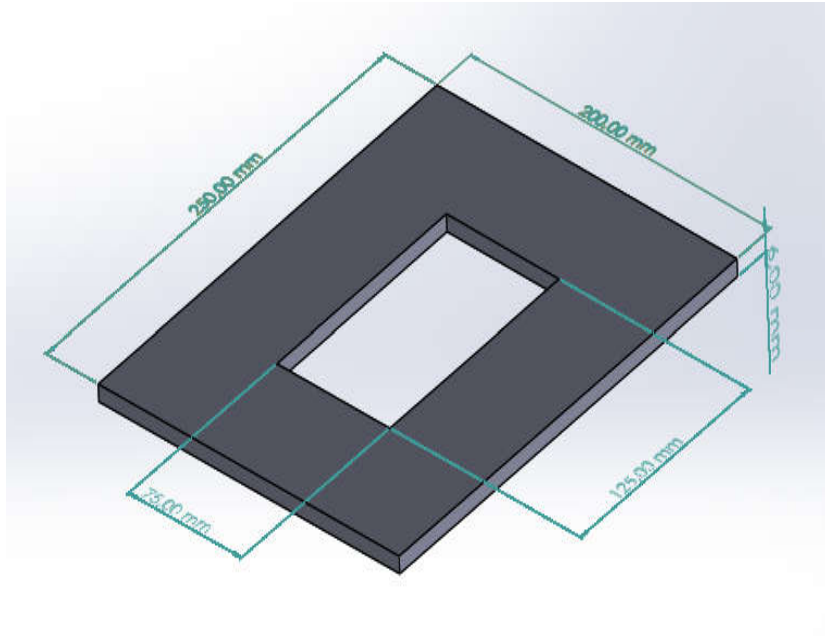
Dimensões do suporte de fixação das placas de compósito.
